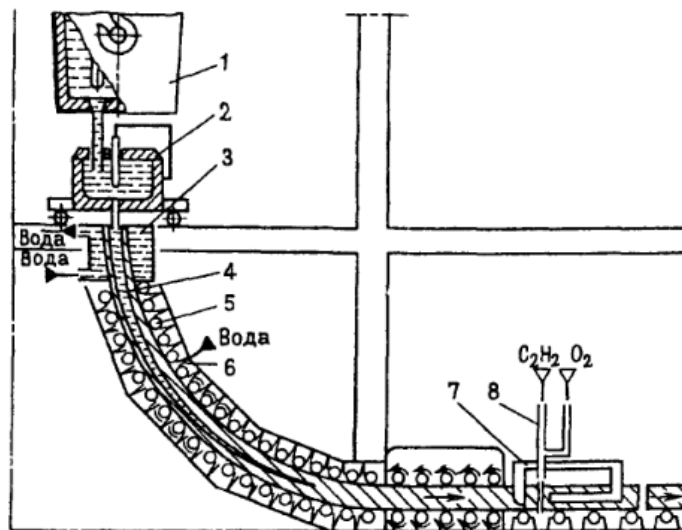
Схема установки для непрерывной разливки стали.
